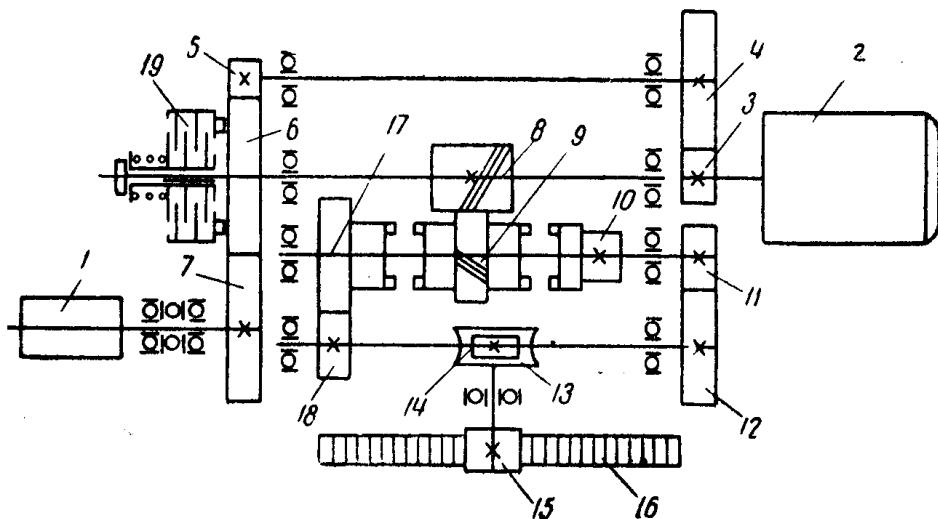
Кинематическая схема длинноходового сверла ЭБР-1:
